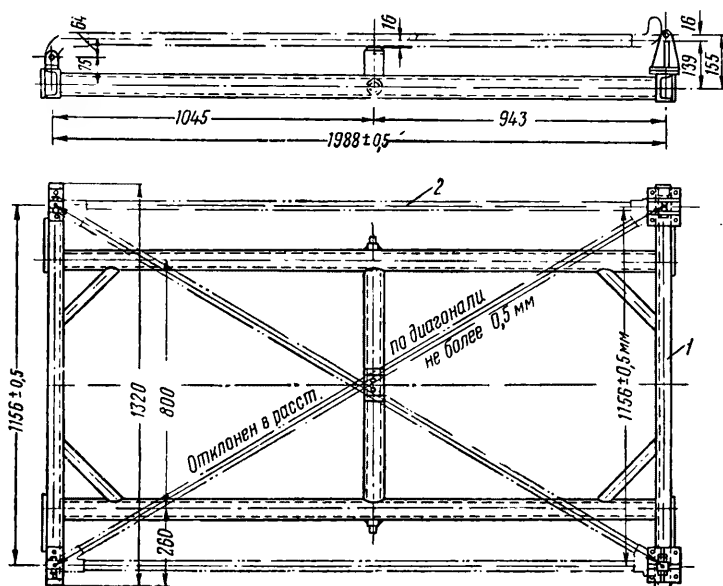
Кондуктор для проверки и сборки верхней рамы пантографа типа ДЖ-4:
